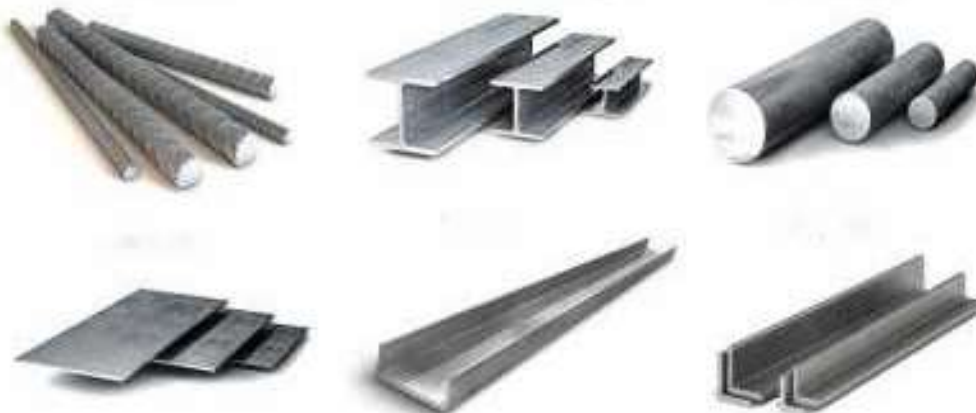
Заготовки сформовані шляхом механічної обробки сортового та спеціального прокату
